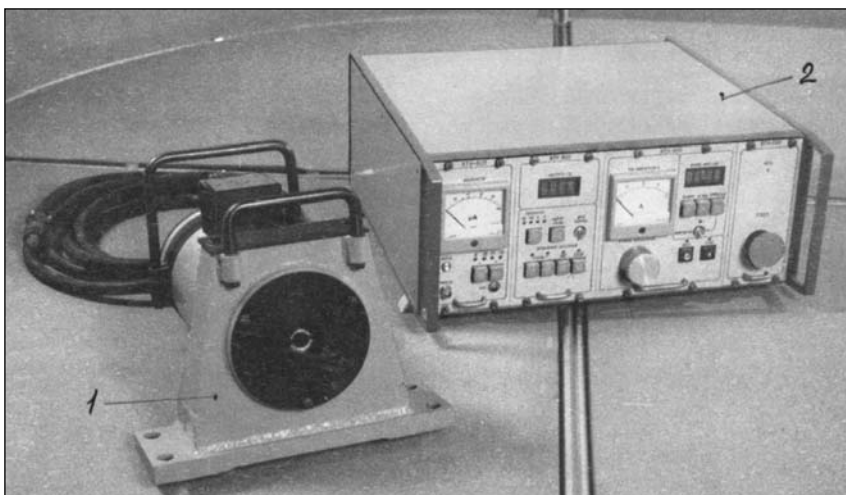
Технологическая система для проведения НВО сварных конструкций и изделий машиностроения:
